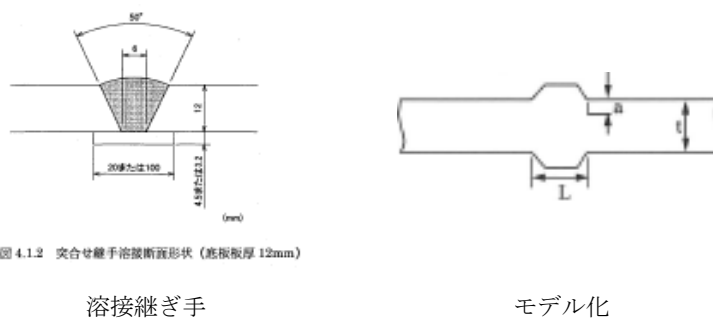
突合せ継手溶接断面形状 (底板板厚 12mm)
